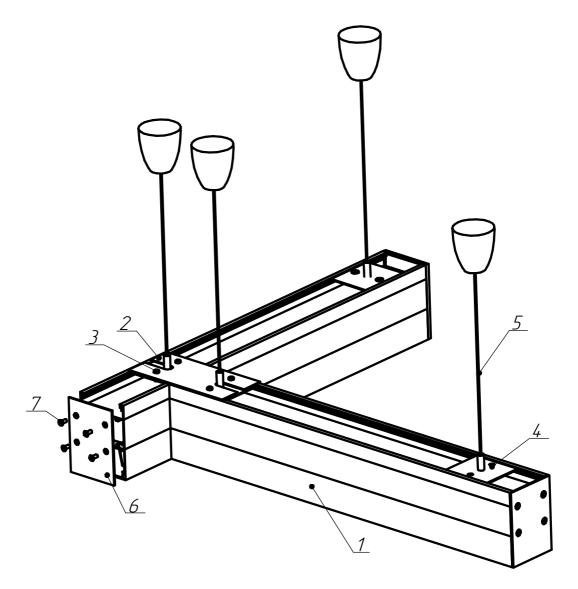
Схема Т-образного соединения светильников 1- светильник, 2- пластина соединительная ДПО02, 3- винты, 4- пластина подвеса, 5- тросовый подвес, 6- торцевая крышка, 7- саморезы
